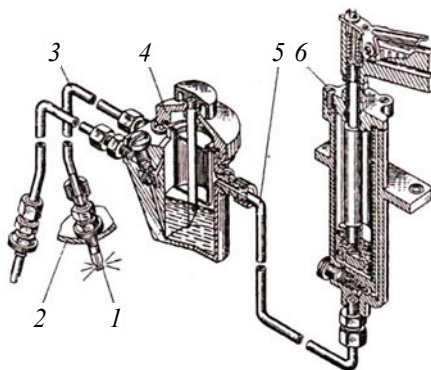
Схема устройства пускового приспособления 5ПП-40А:
